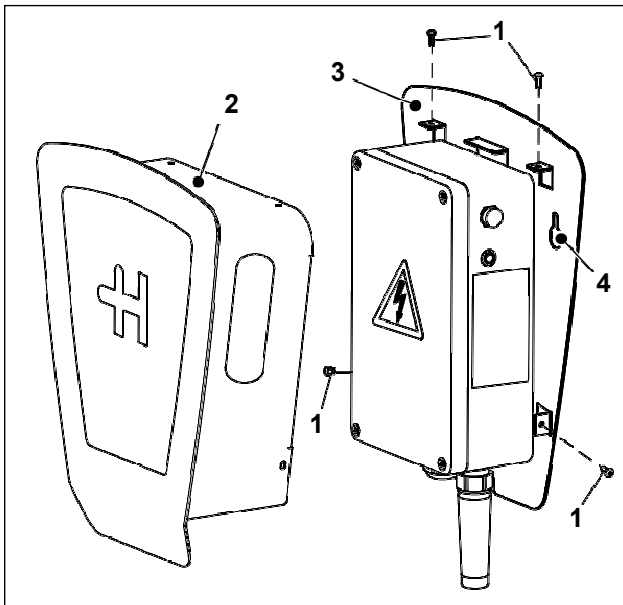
EVC-W1-ECO5M Wallbox Home Eco con caperuza de protección
